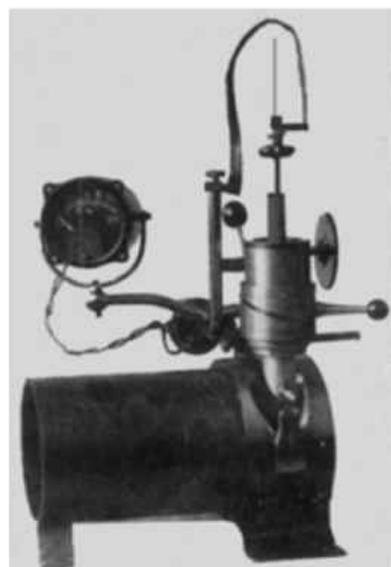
Устройство для извлечения сломанного инструмента в корпусах ракетных снарядов для ракетных установок «Катюша» (начало 40-х гг.)
